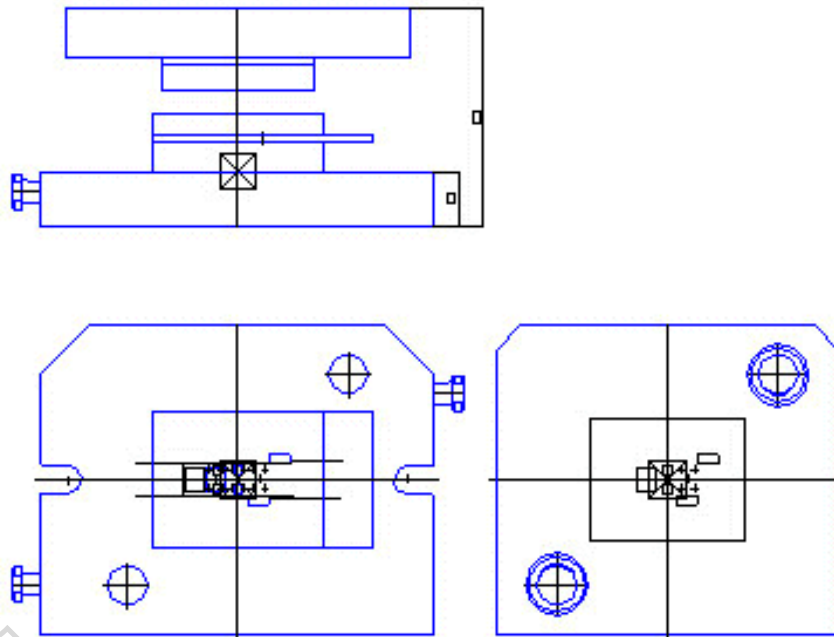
Вид сборочного чертежа после привязки блока к прессу
